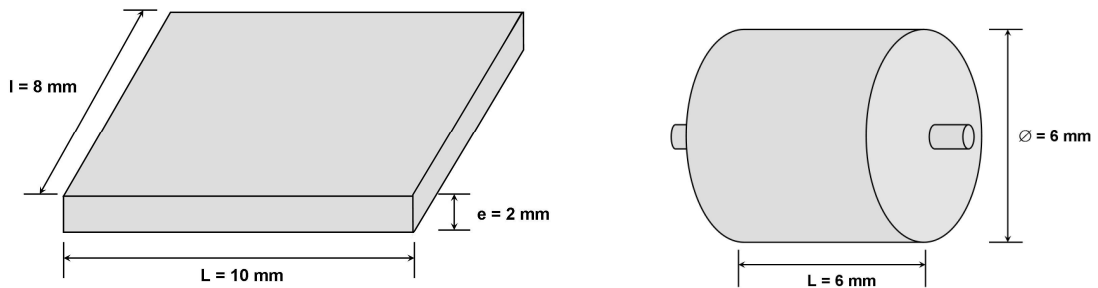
Schémas du plan et du cylindre utilisés pour l'essai de frottement
